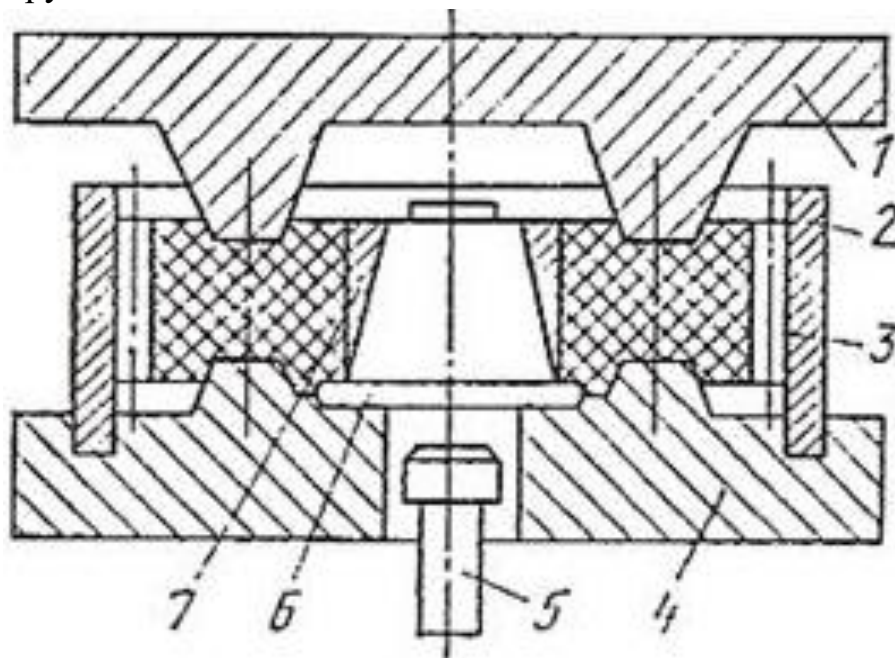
Принципова схема штампа для відновлення шестерень способом пластичного деформування: 1 - пуансон; 2 - обмежувальне кільце; 3 - шестерня; 4 - матриця; 5 - викидач; 6 - центруючий конічний вкладиш; 7 - розрізана конічна пружна втулка
